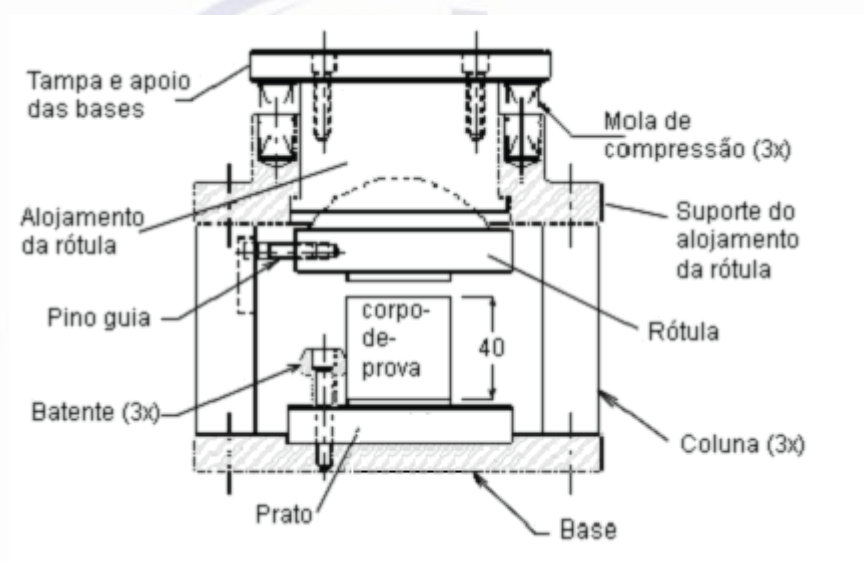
Dispositivo de carga típico para ensaios de resistência à compressão
